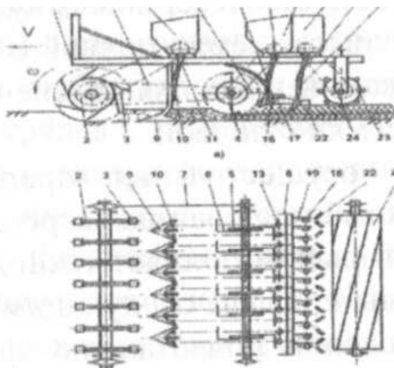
Комбинированный агрегат для обработки почвы и посева:
